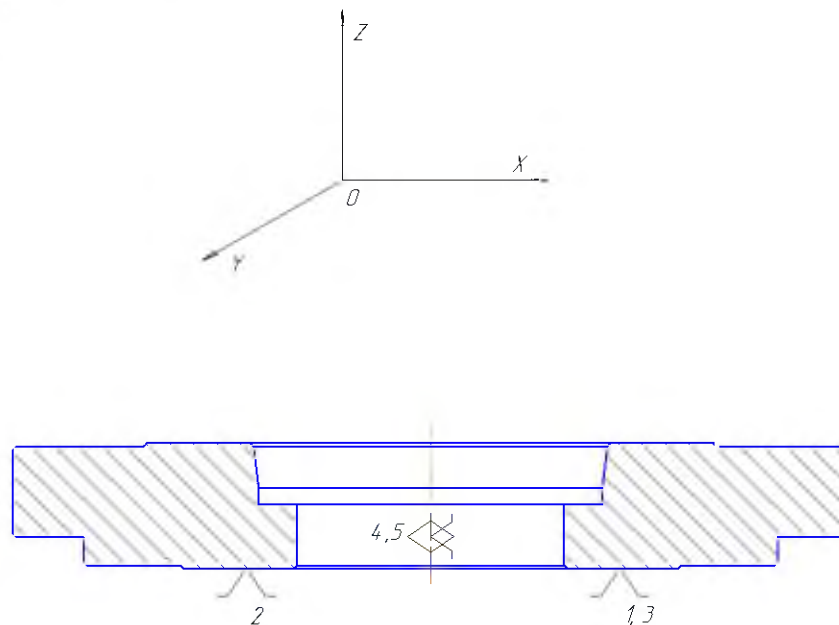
Схема базування при обробленні лівого торця та виконання внутрішнього конічного отвору фланця
